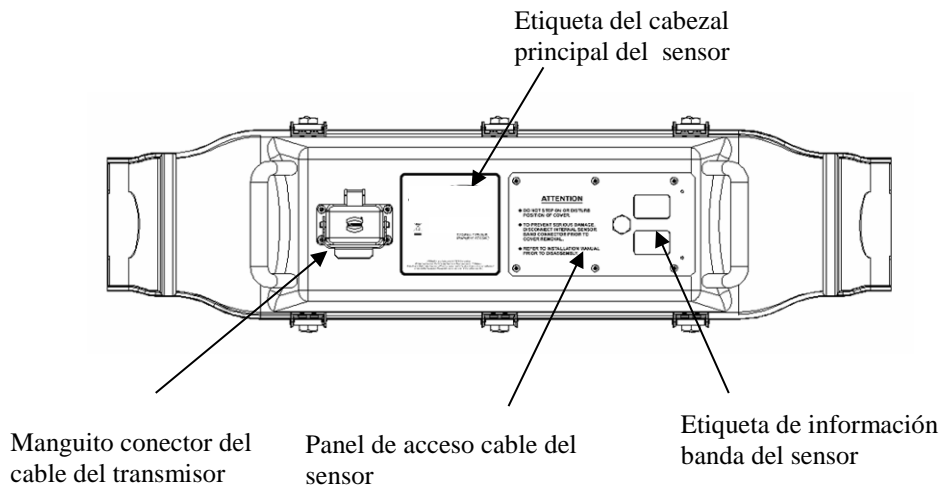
Vista exterior del conjunto de la cubierta superior del sensor
